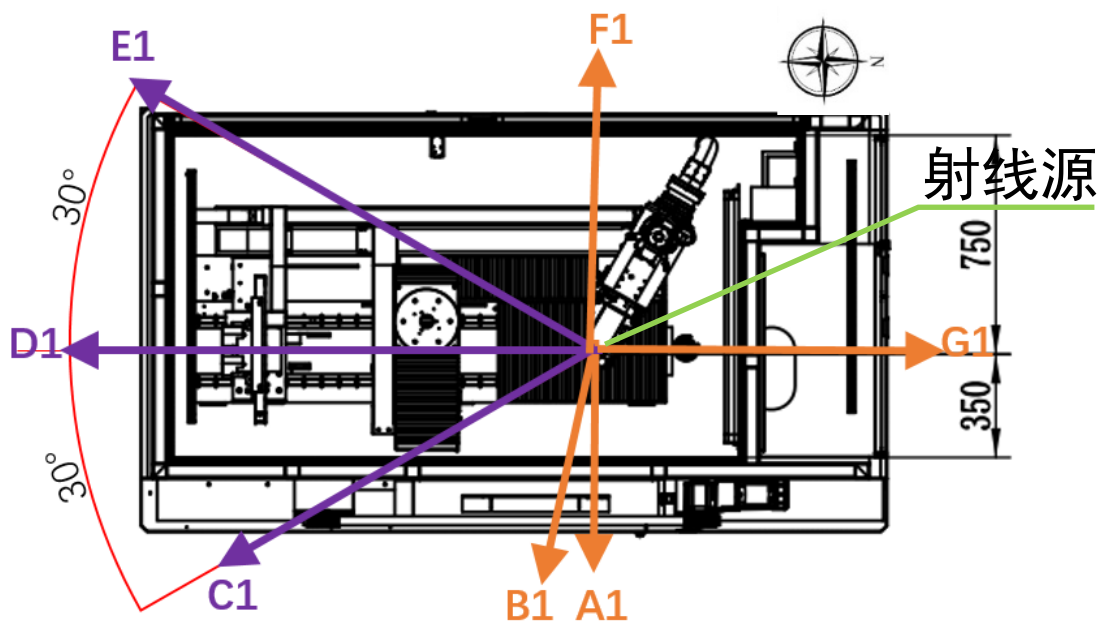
FXO-CT2000 型工业 CT 辐射屏蔽计算预测点位平面图 (单位: mm)
